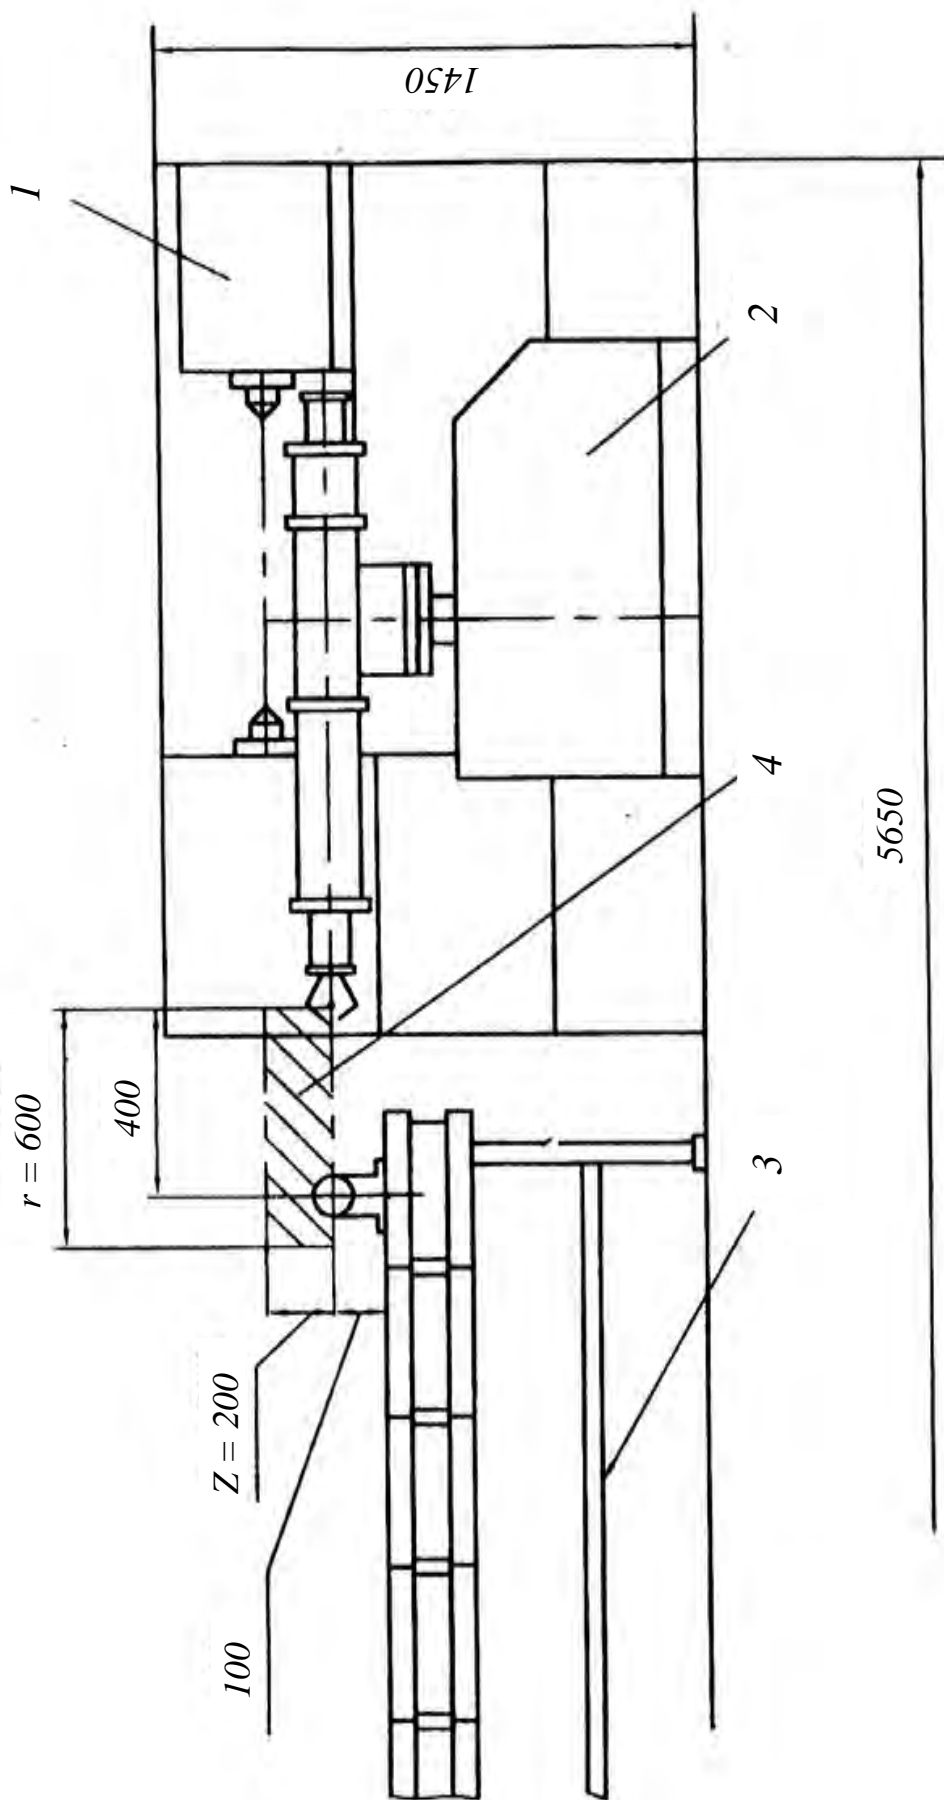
Компоновка РТК линейного типа (вид сверху)
